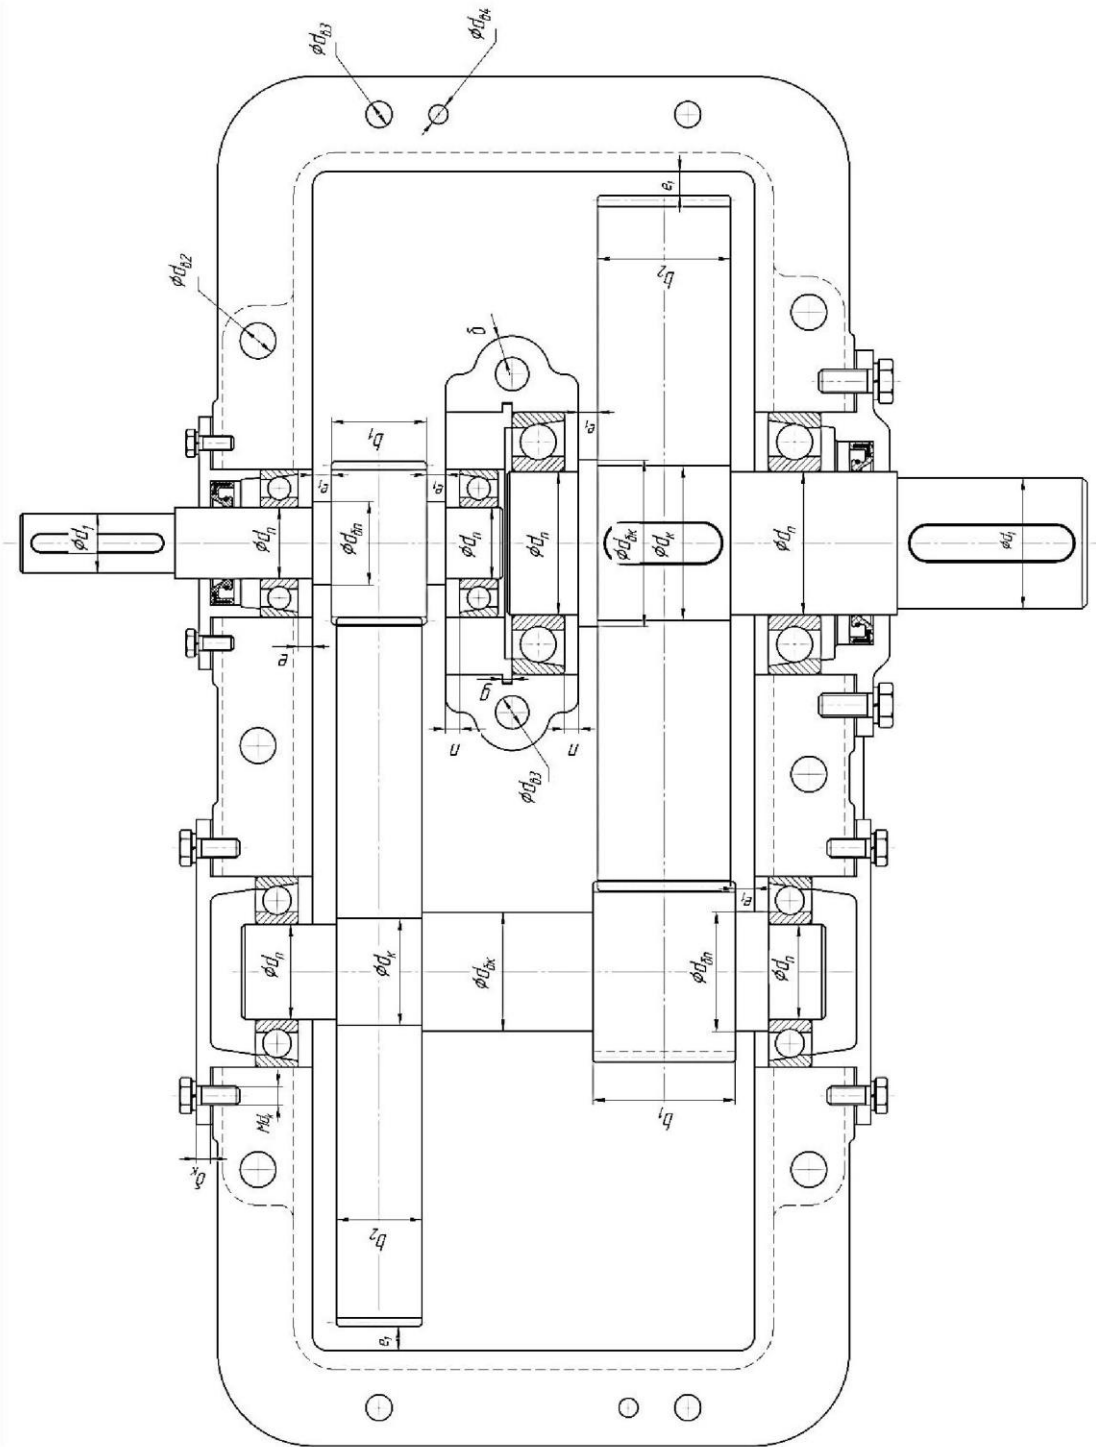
Компонувальне креслення співвісного циліндричного редуктора (закінчення)
